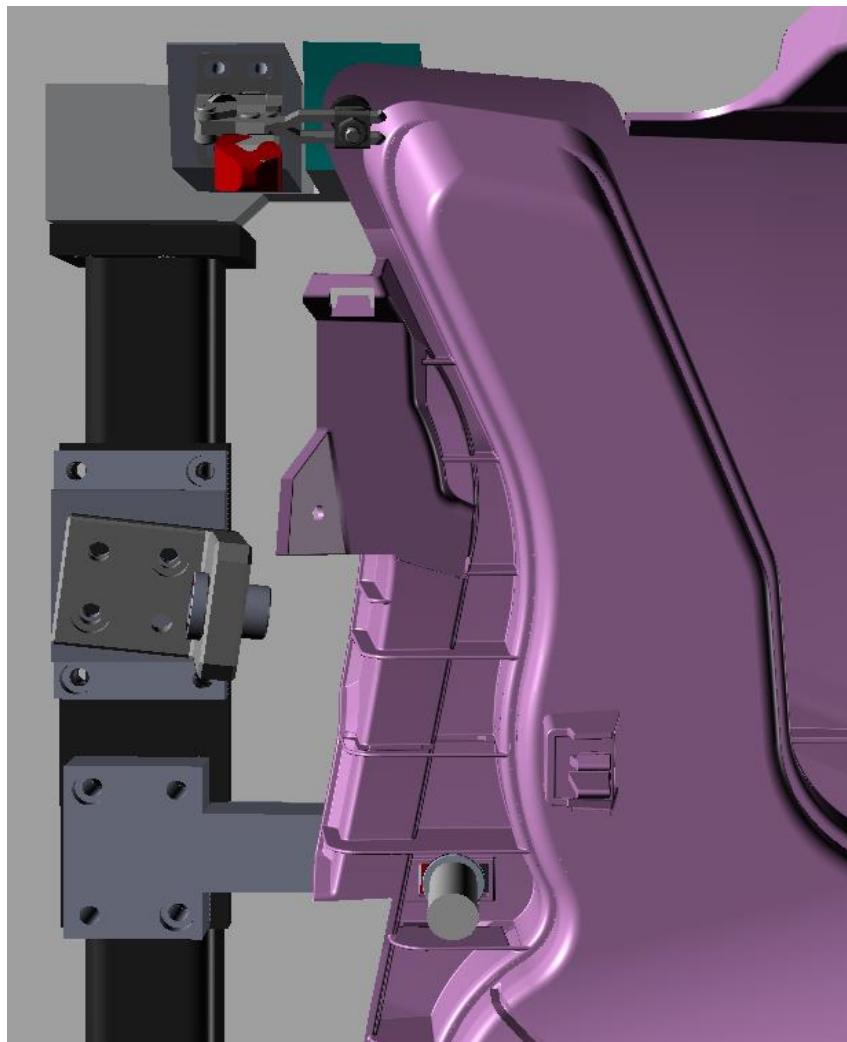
CAD Pieza del posicionador para RPS (X1-X2-Z1-Z2-Z6-Z7)
